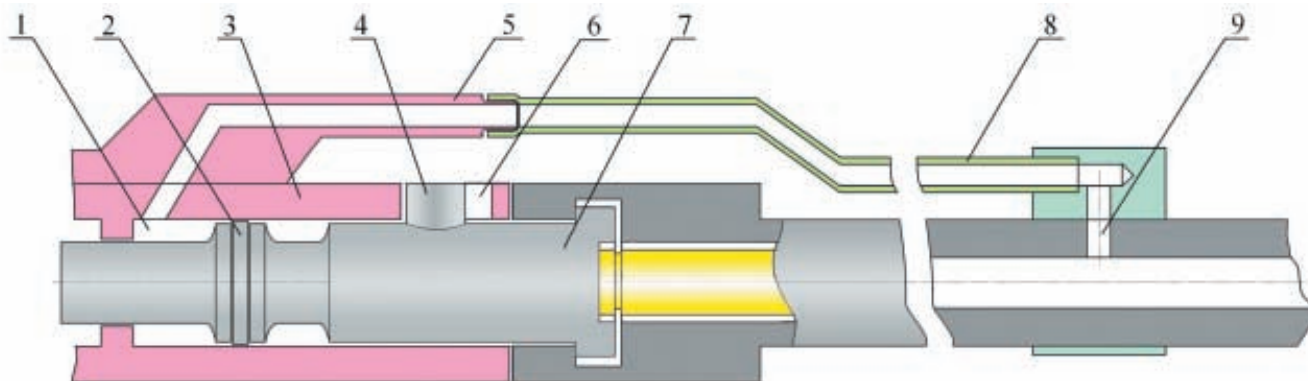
Схема БГД автоматической винтовки М16А2. Исходное положение деталей автоматики.
